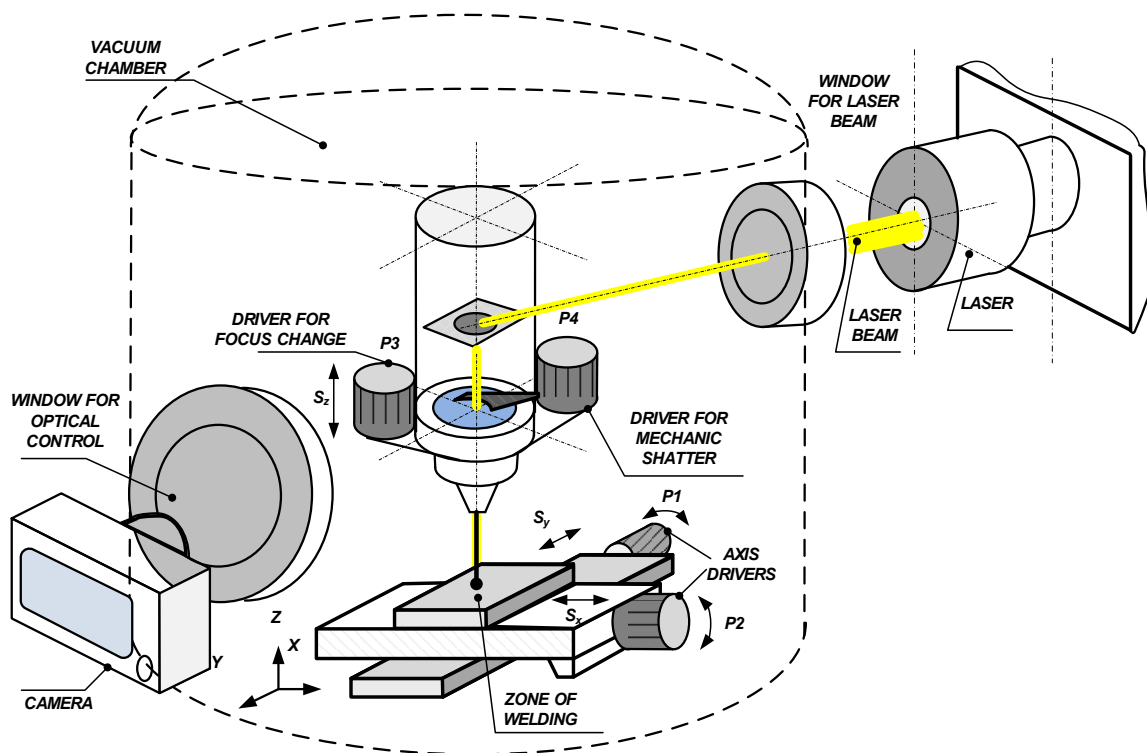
Схематичне зображення установки для обробки ВВКМ
